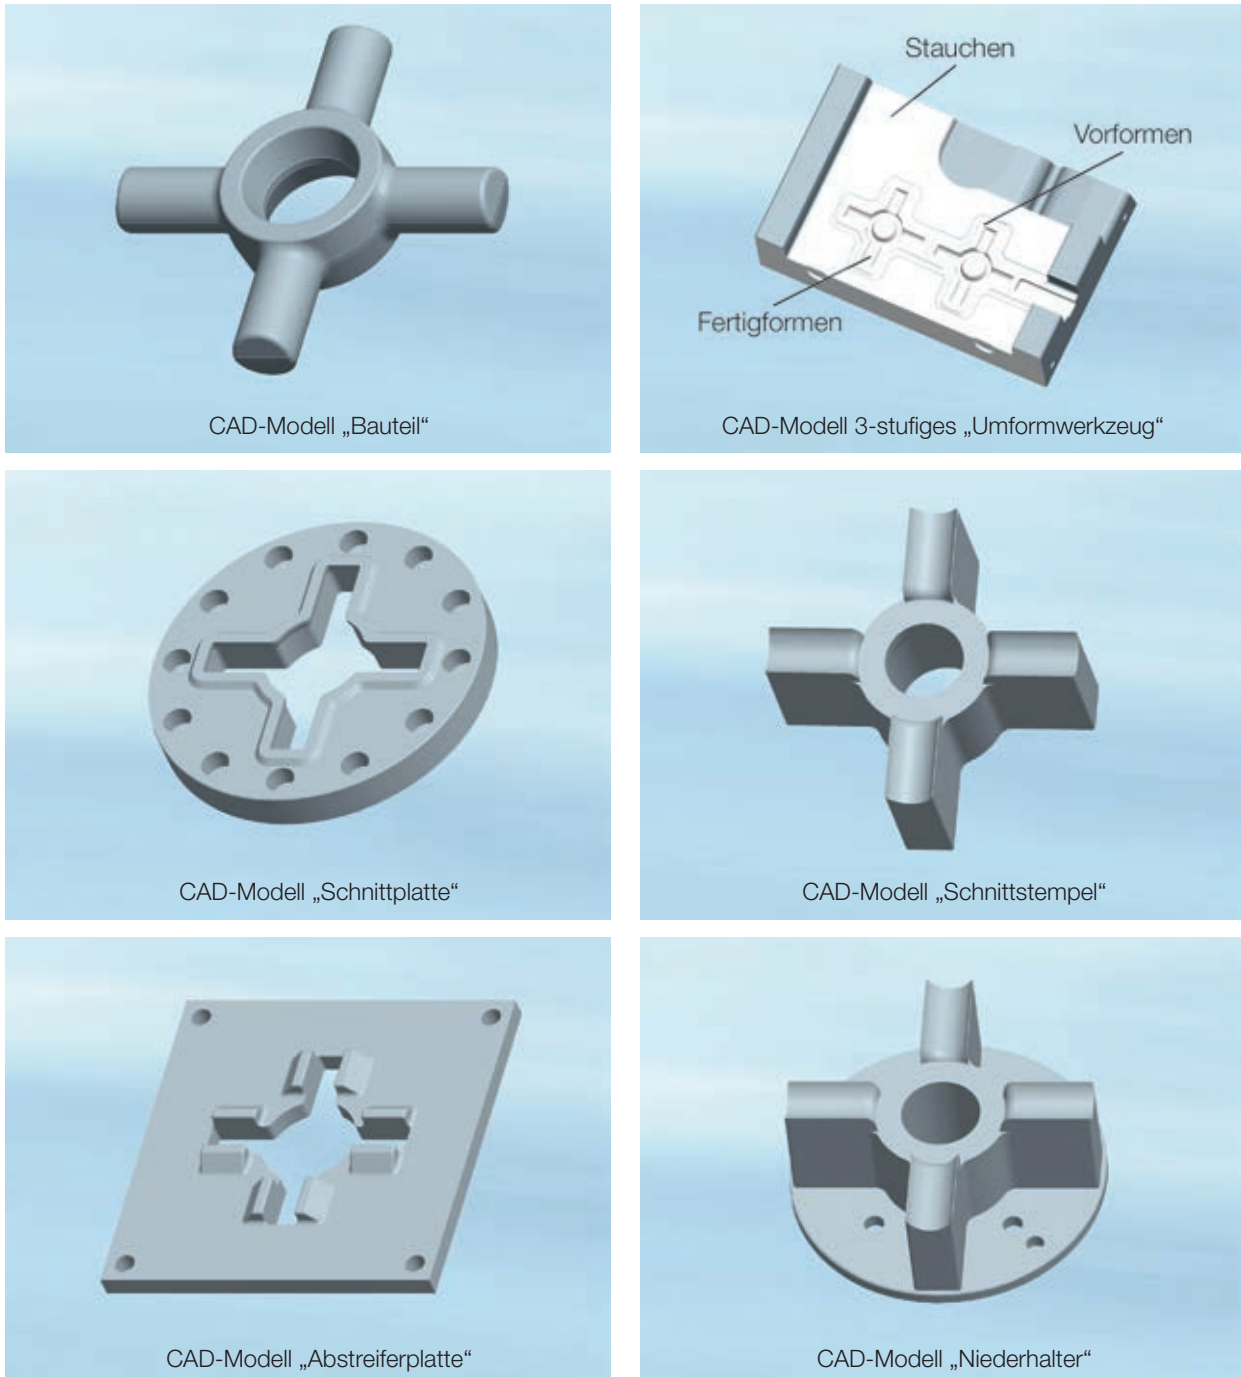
Vollständiges 3D-CAD-Modell für ein Kreuzgelenk und zugehörige Aktivwerkzeuge
